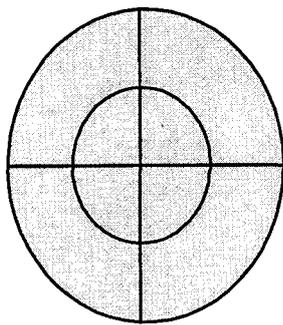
Front cutting 및 Back cutting에 의하여 얻어진 균열부위
